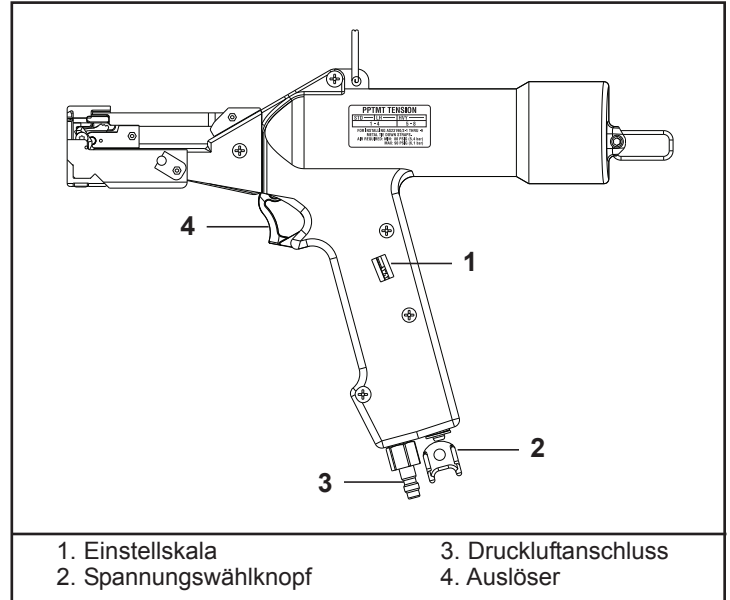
Pneumatisches Abbindewerkzeug PPTMT
